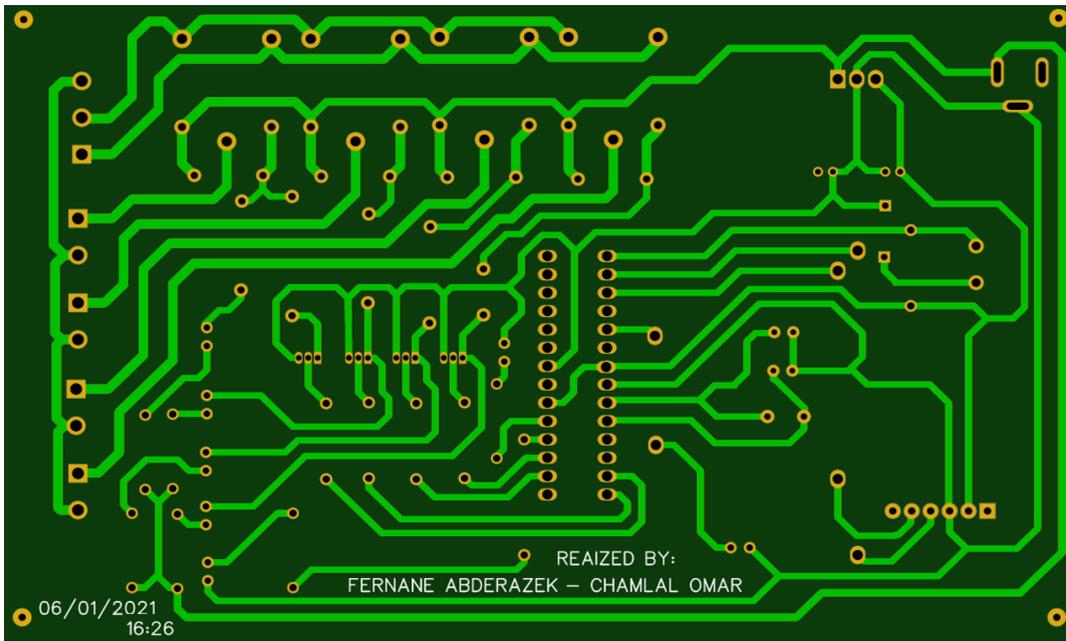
Phase Arrière De la Carte PCB en 2 Dimensions
